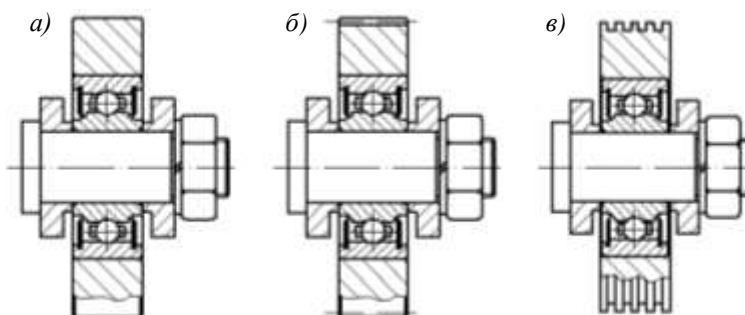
Конструкции полюсного наконечника с гладкой рабочей поверхностью (*а*), с поперечными (*б*) и продольными (*в*) пазами
